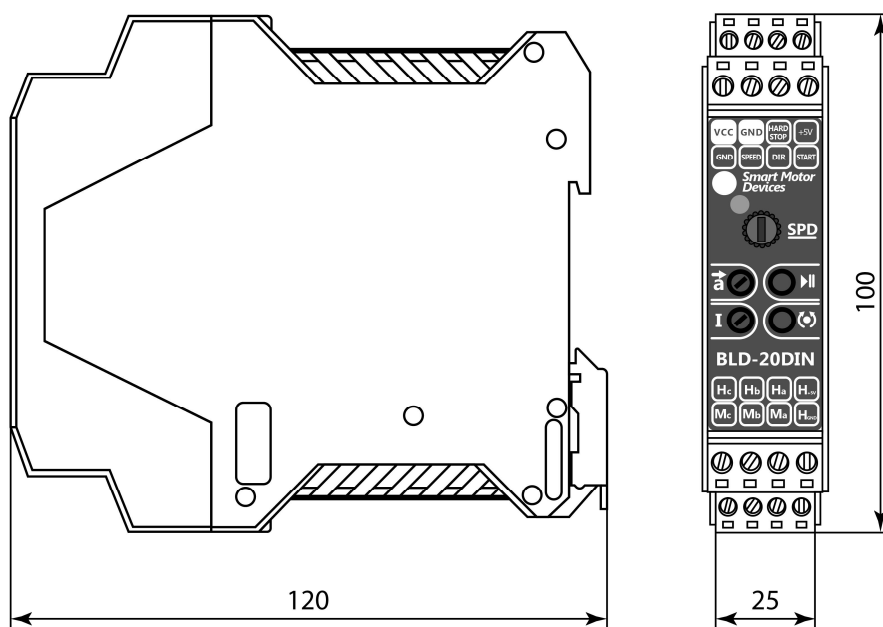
Габаритные и присоединительные размеры блока БУВД-20К.
